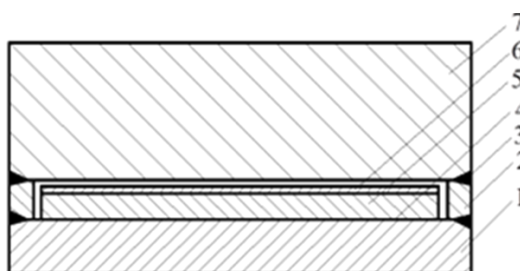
Конструкція несиметричного пакета. 1 – кришка; 2 – з'єднувальні планки; 3 – зварні шви; 4 – розділовий шар; 5 – плакучий шар; 6 – проміжний підшар; 7 – основний шар [13]
